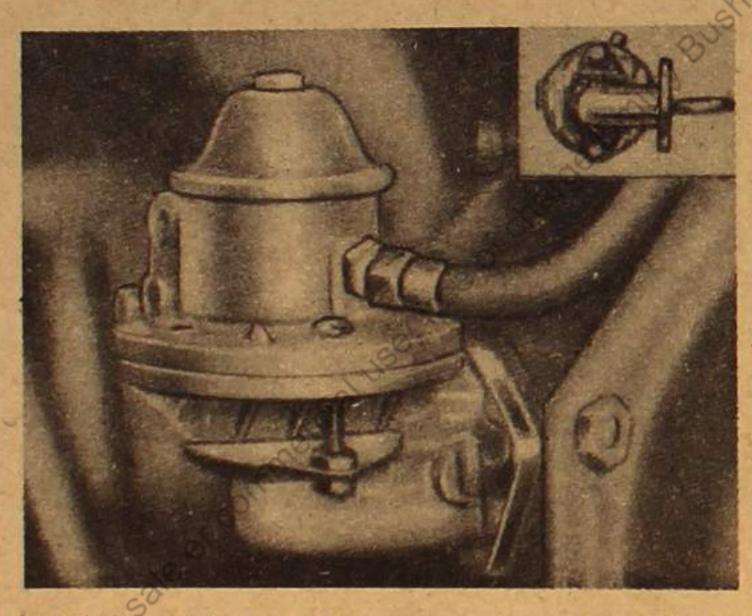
Einstellbohrungen im Kraftstoffs pumpen=Gehäuseunterteil durch einen mit Filz ausgefüllten Halter abgedichtet.
